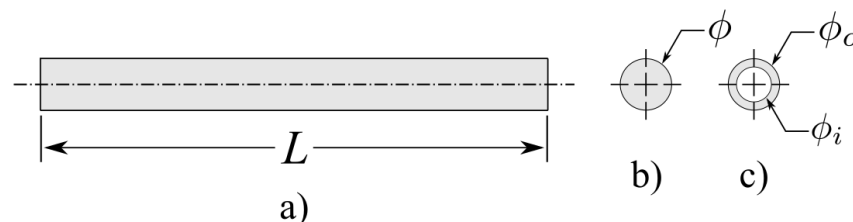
Variables geométricas del eje: a) longitud, b) diámetro de la sección transversal sólida y c) diámetros exterior e interior de la sección transversal hueca.
